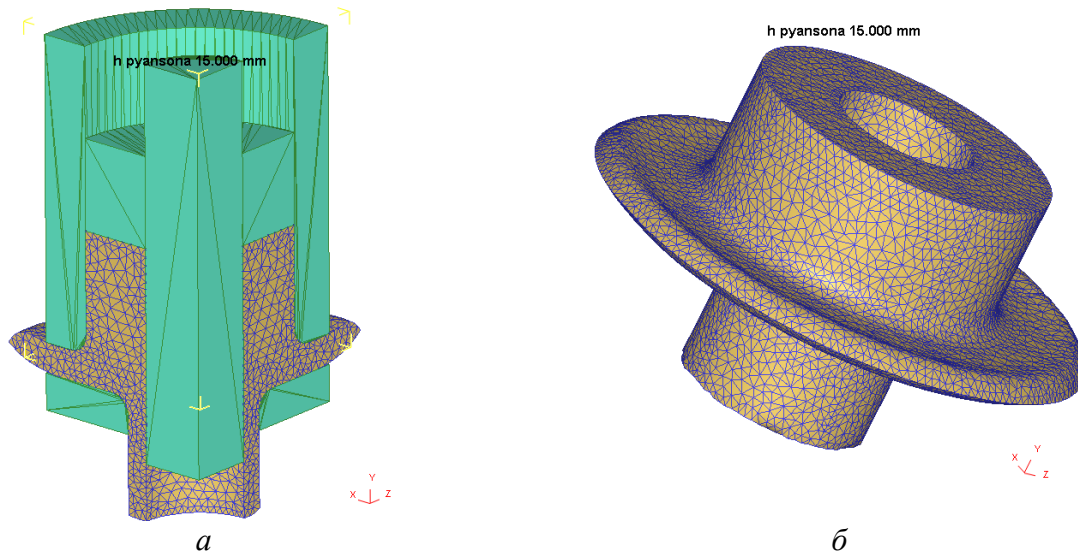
Модель системи інструмент-заготовка (а) та деталь на заключній стадії комбінованого видавлювання (б)
